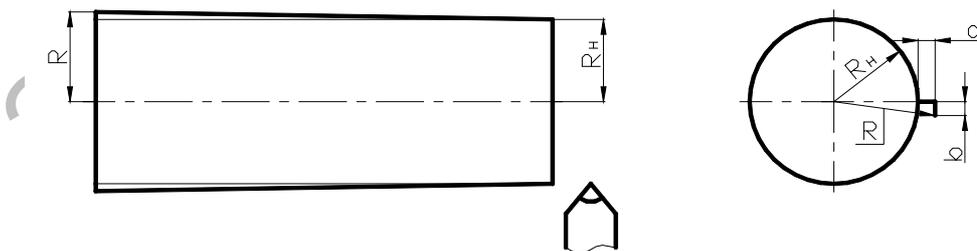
Форма поверхности при односторонней токарной обработке (резец расположен перед линией центров)
